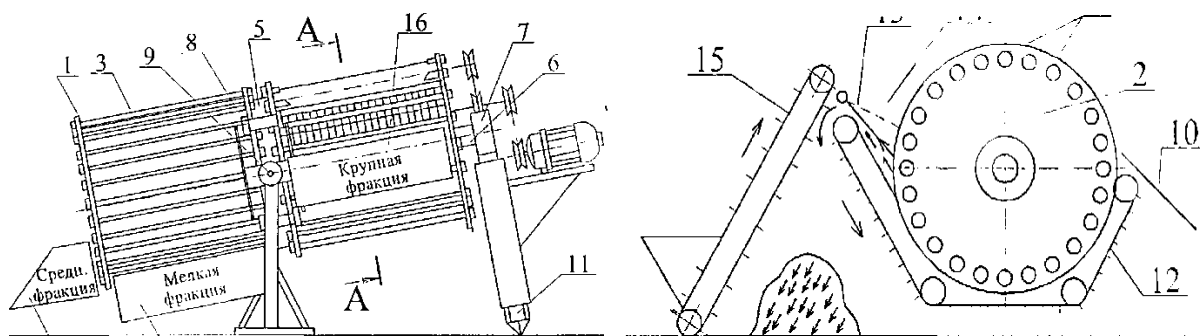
Устройство для очистки и сортировки корнеклубнеплодов:
